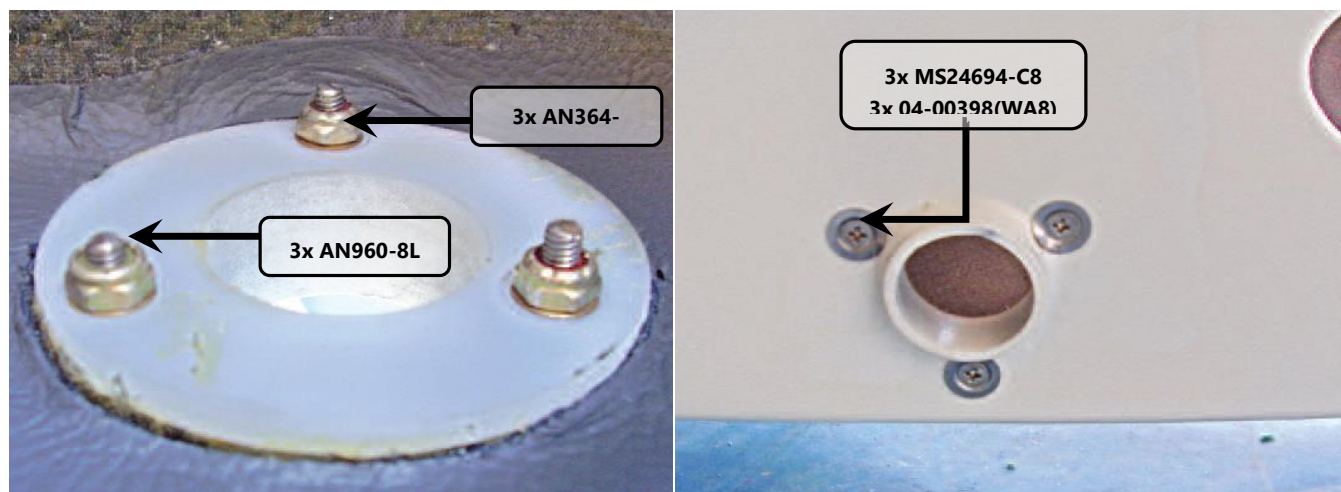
Flange de teflon (vista interna e externa à cabine)
